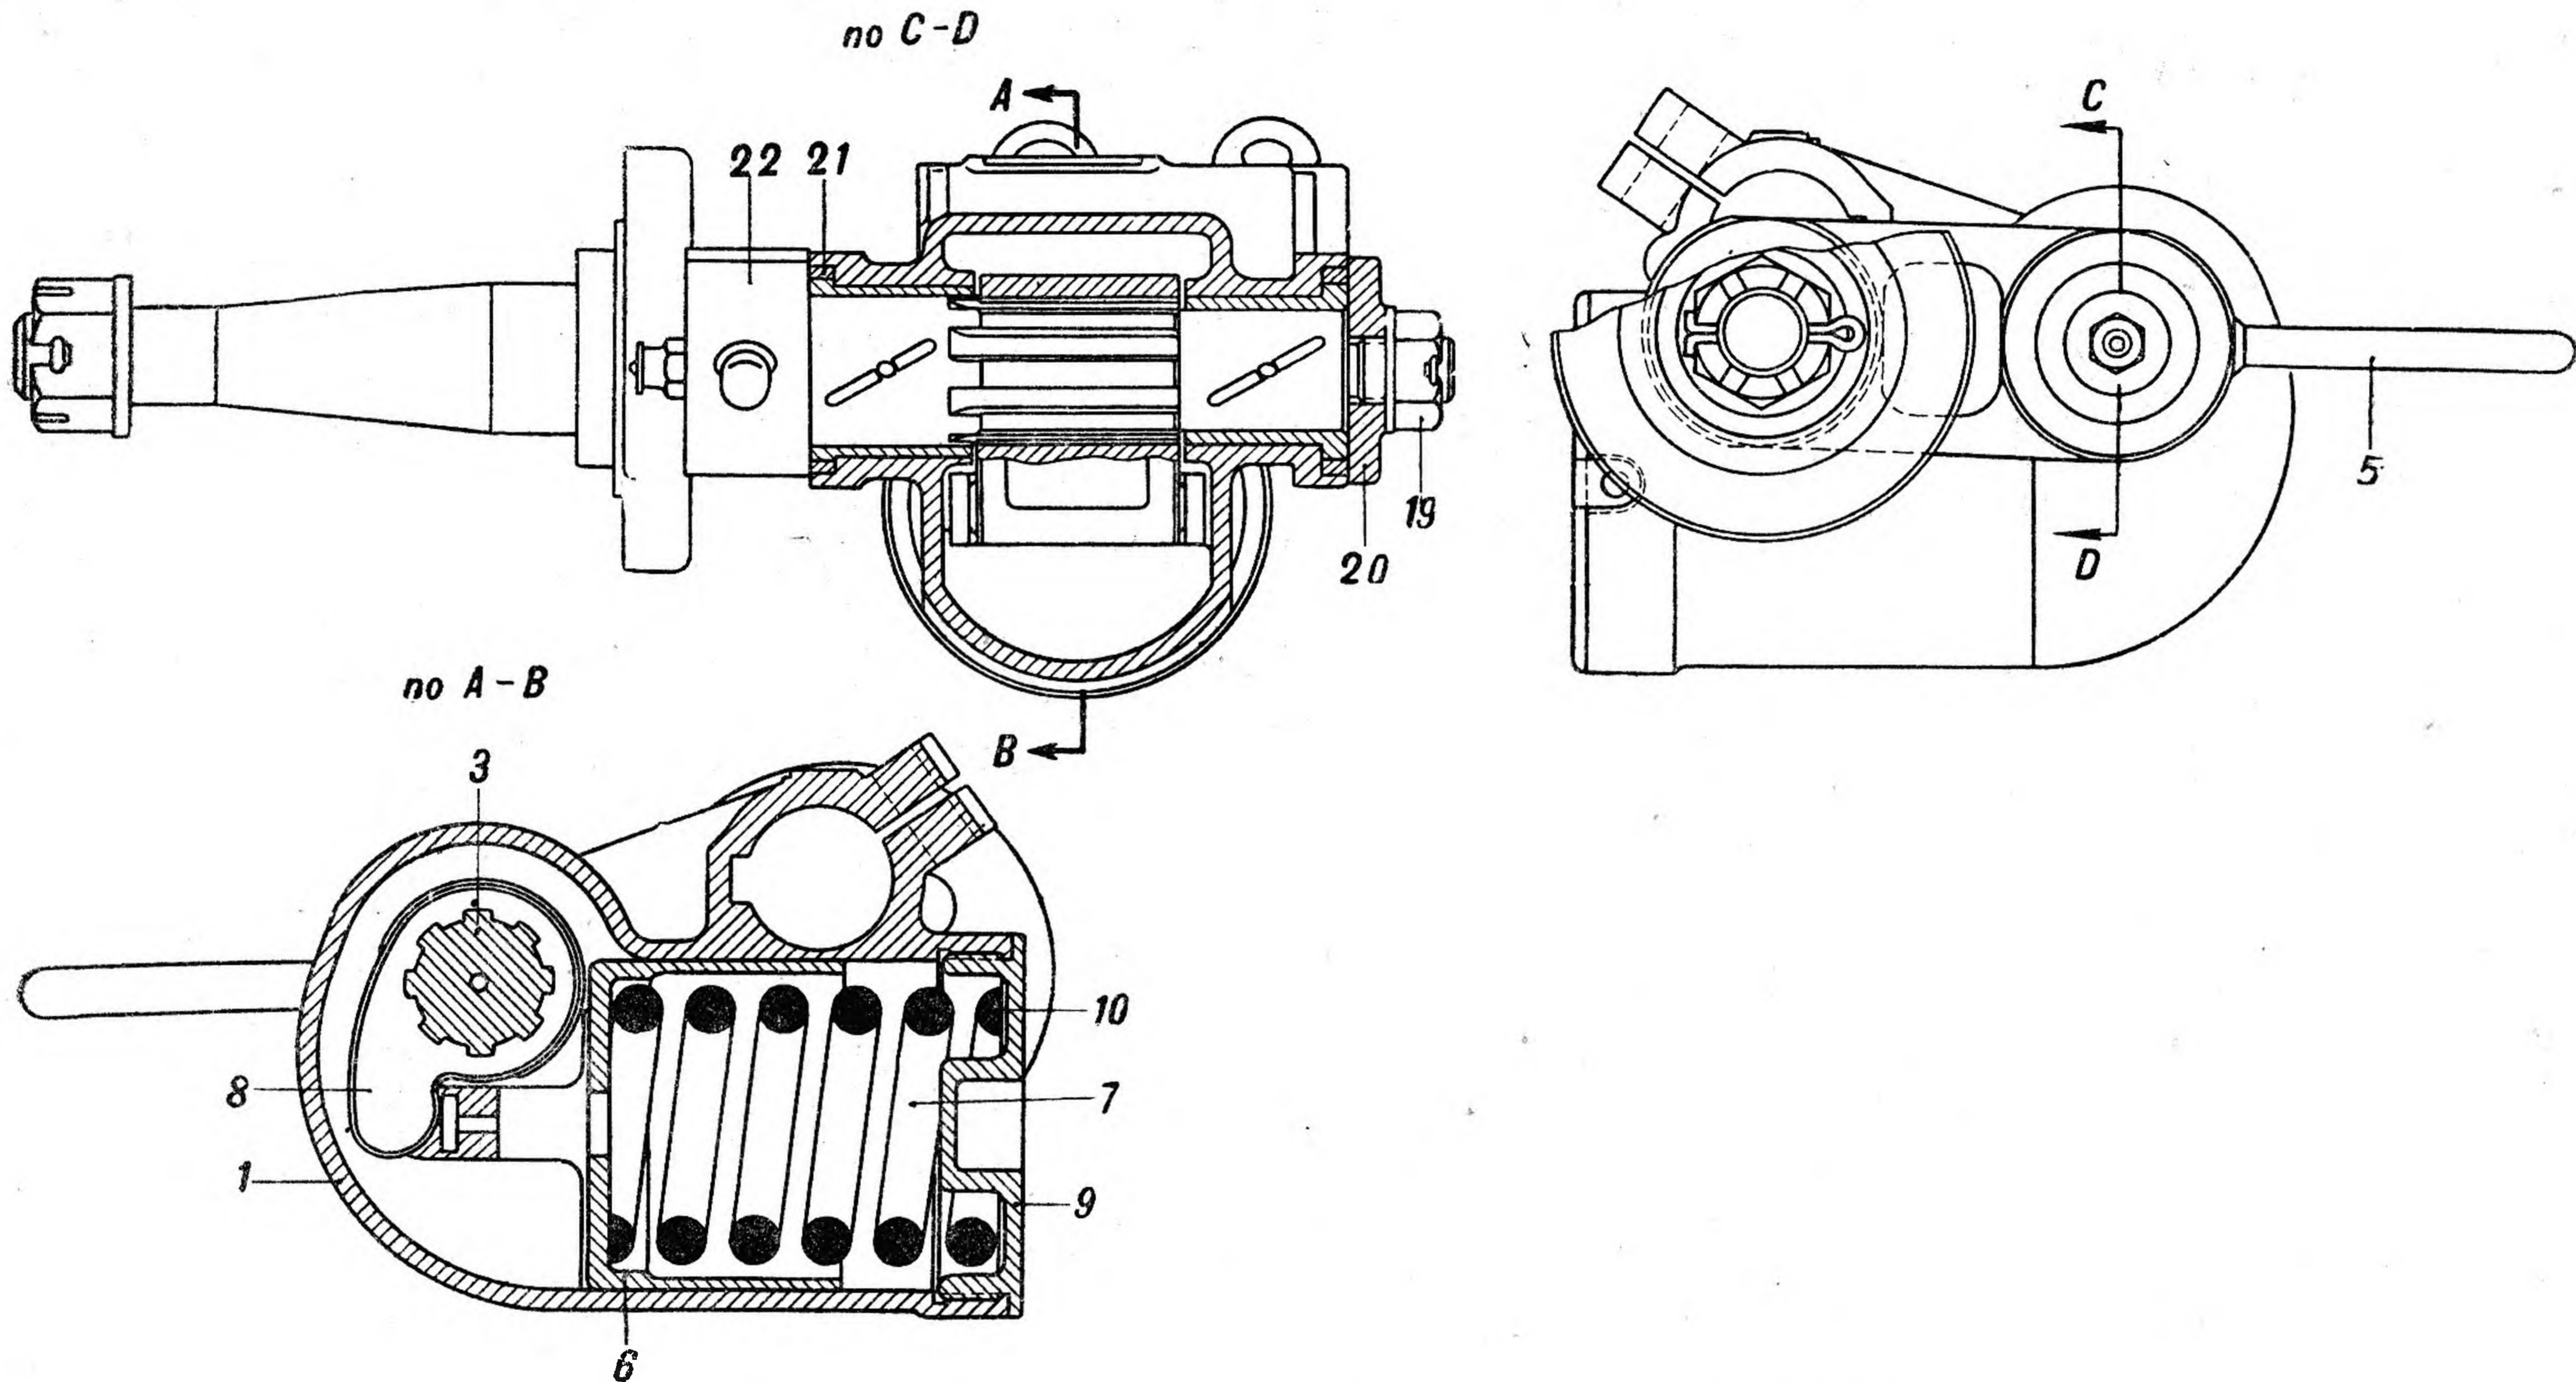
Коробка механизма подпрессоривания левая с кривошипом
